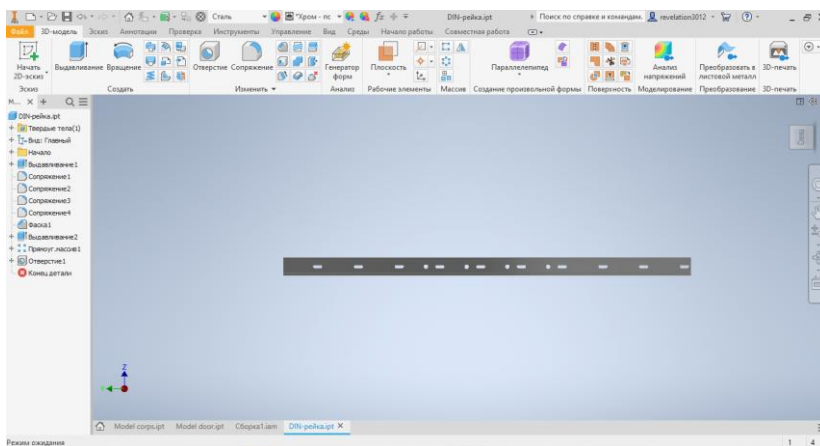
Отримані отвори для болтового з'єднання DIN-рейки
